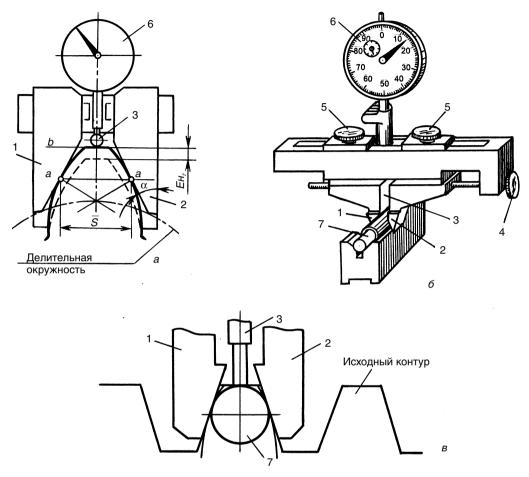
Зубомер смещения: а — схема измерения; б — общий вид зубомера; в — схема настройки
